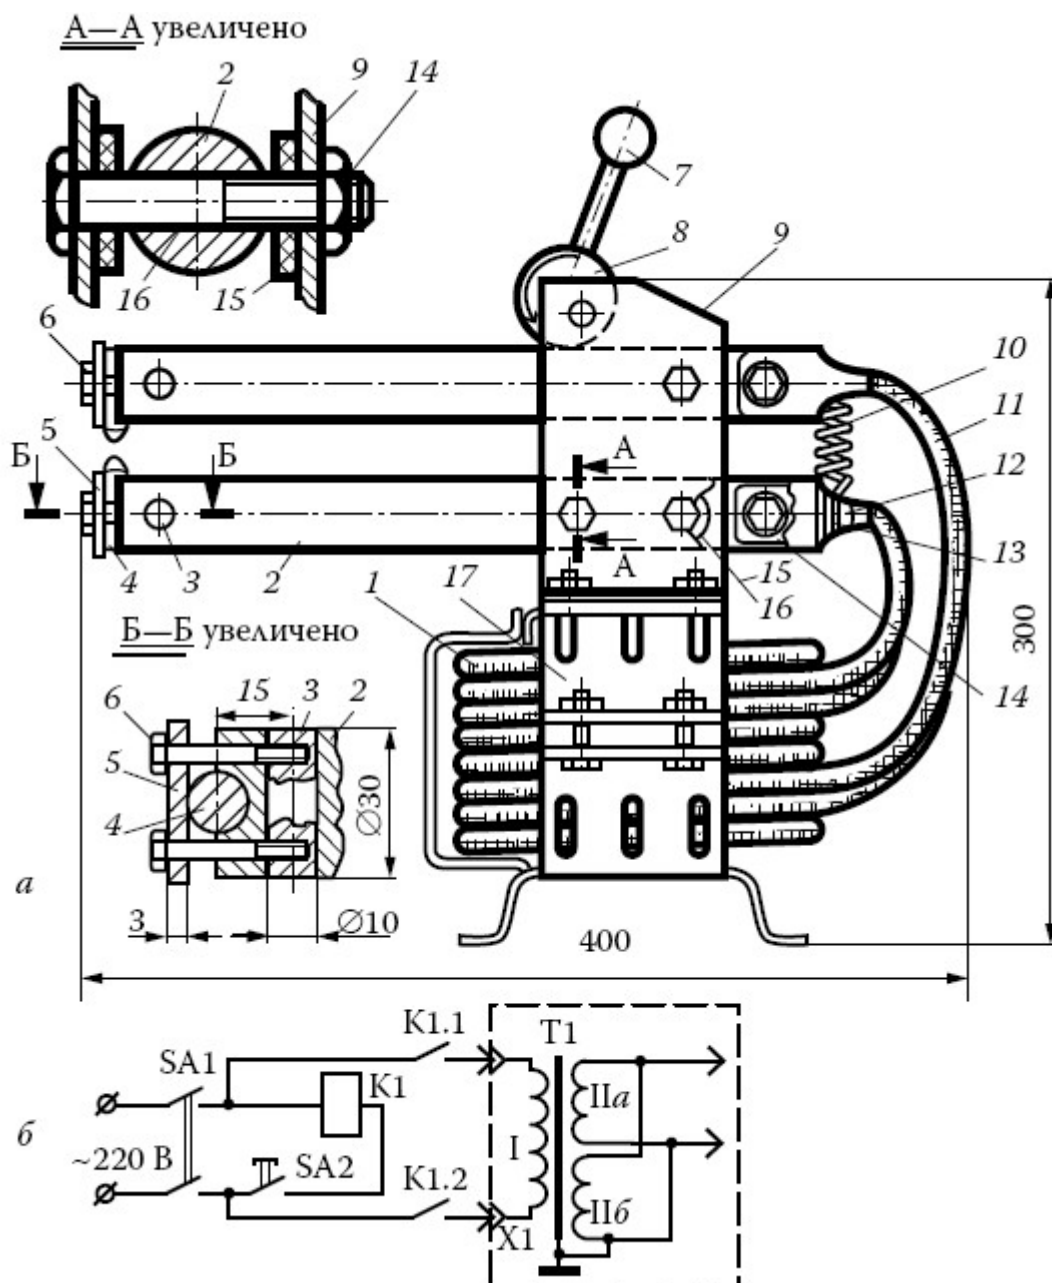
Аппарат для точечной сварки листовой стали:
